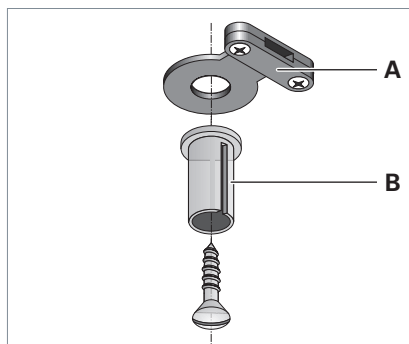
Montaggio dell'elemento di fissaggio al soffitto.
